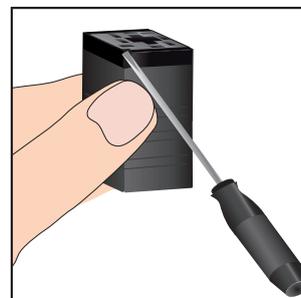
Entfernen des Steckverbinder-Klemmblocks
